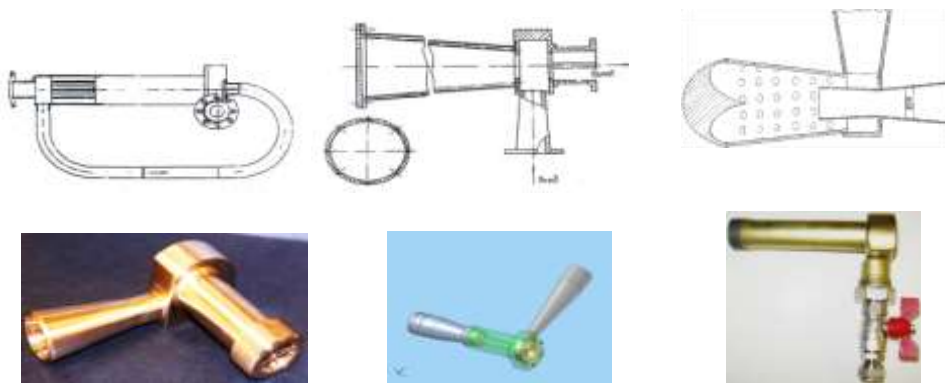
Вихревой гидрокавитатор – варианты конструктивных схем и конструкций
